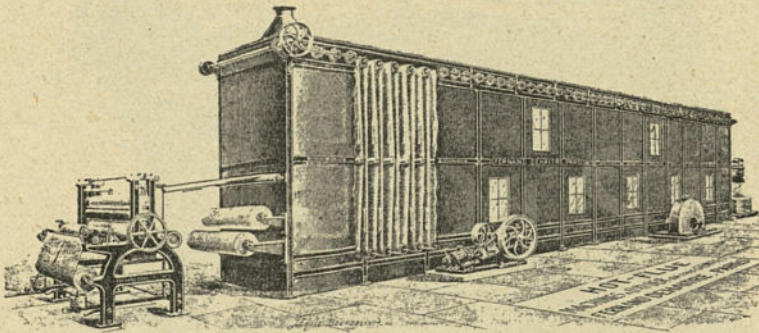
Vue d'ensemble d'un hot-flue (Dehaitre).
